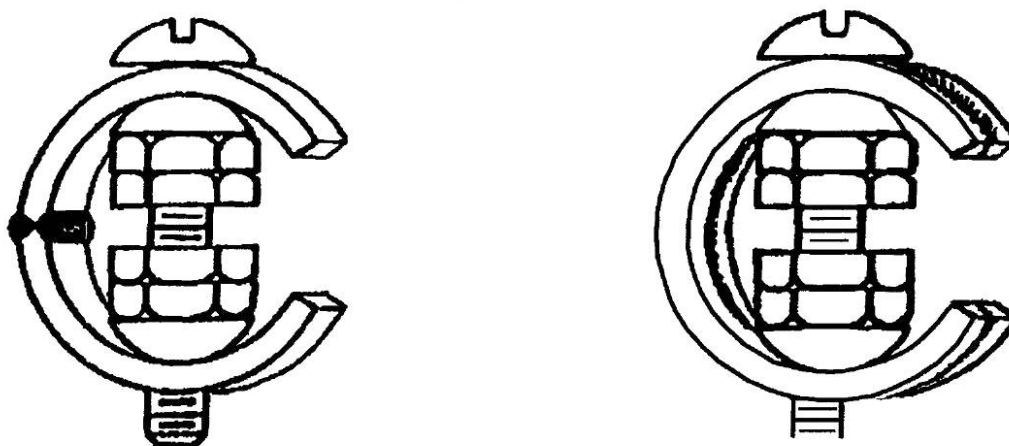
С-образные образцы с продольным (слева) и кольцевым (справа) сварным швом
